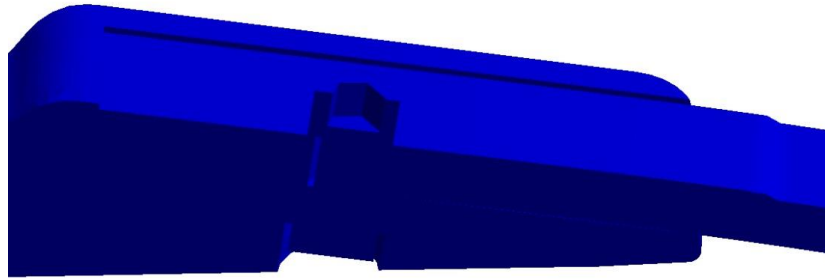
Corte de la sección transversal de la unión apernada. (Propia, 2020).
